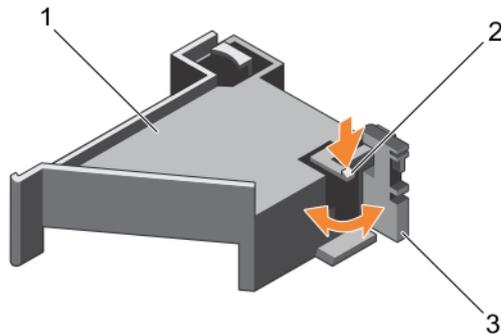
Como abrir e fechar a trava do suporte da placa PCIe
